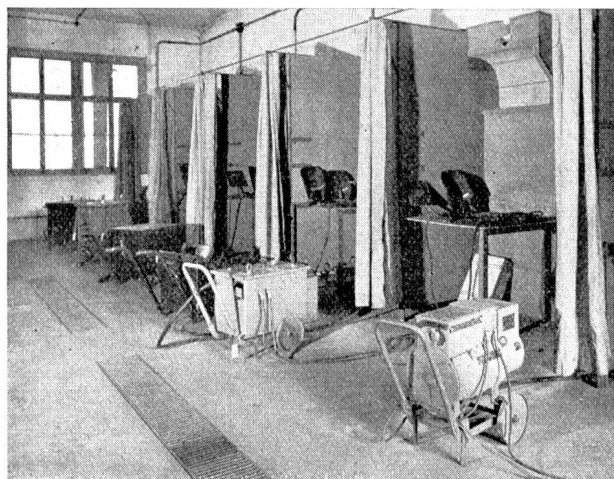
Schweiß-Lehrwerkstätte des Elektrizitätswerks Basel. Ansicht der Schweißkochen mit Schweißumformern und -transformatoren.
